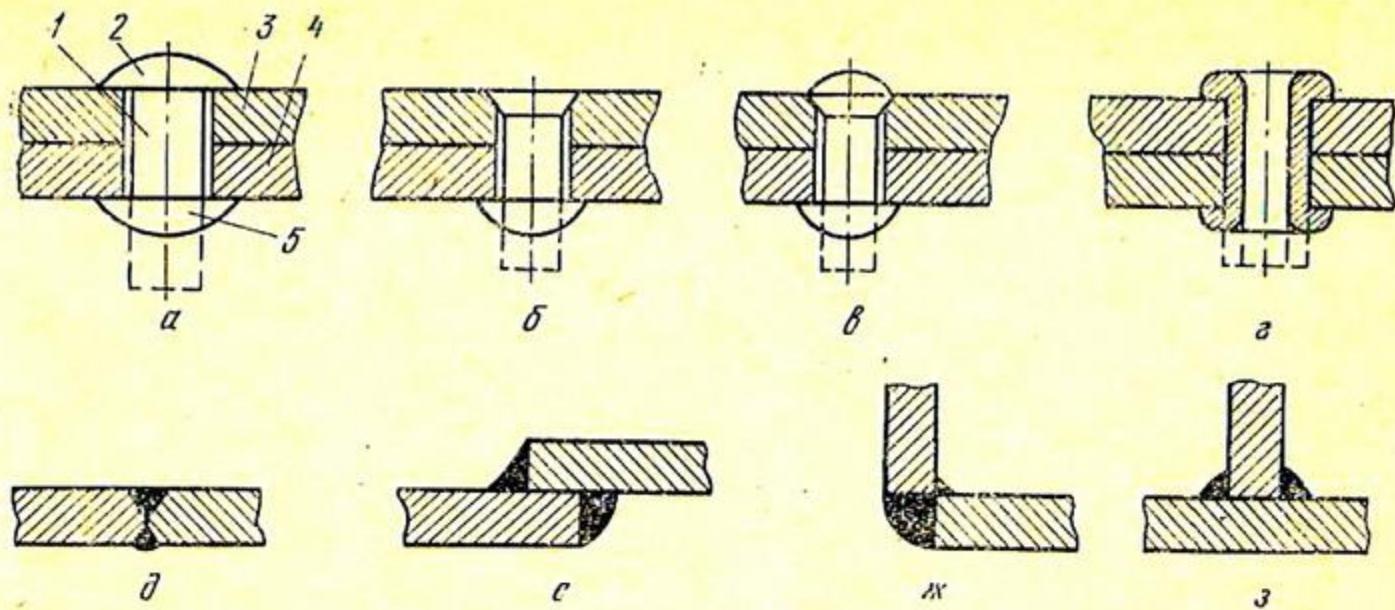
Неразъемные заклепочные и сварные соединения
